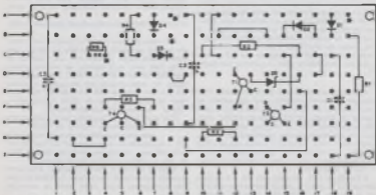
Posição dos componentes do circuito I na chapa de PCB impressa.
